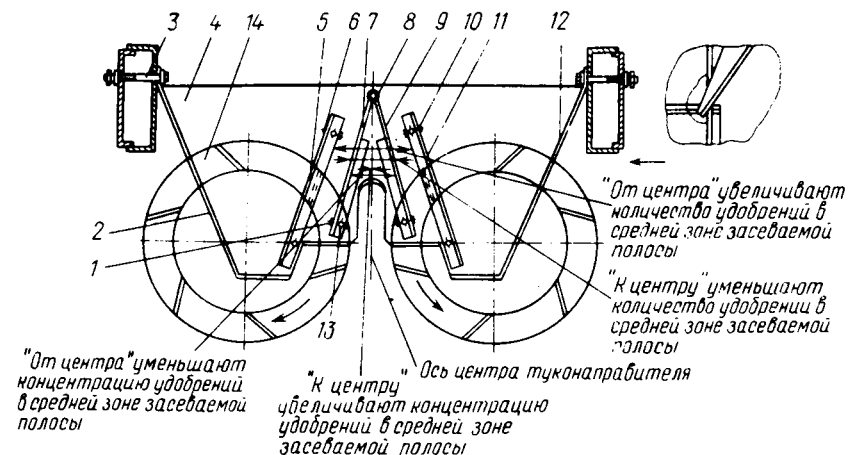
Регулировка равномерности внесения удобрений по ширине захвата СТТ-10:
